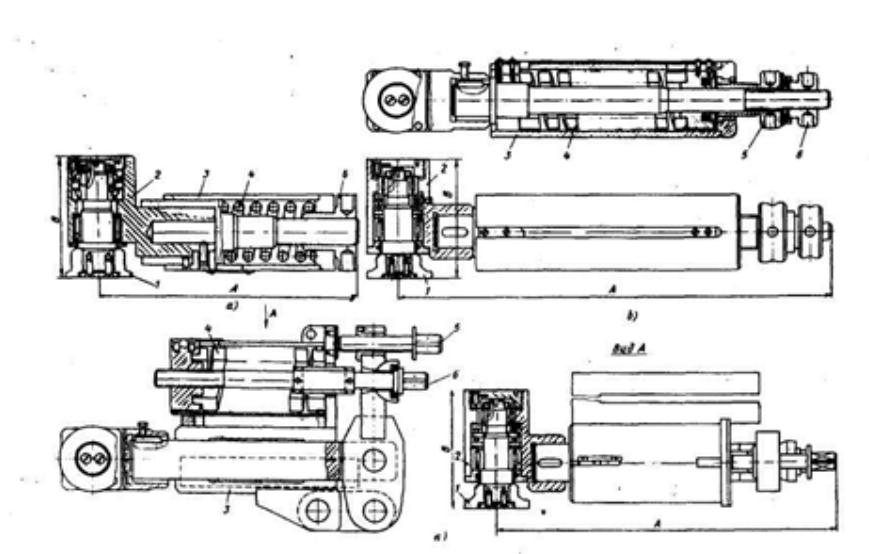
Однороликові пристрої, що забезпечують великі зусилля обкатування а – 2500-5000 Н; б – 10000-20000 Н; в – 40000 Н
